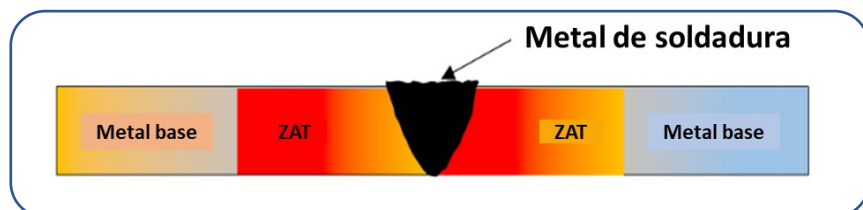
Perfil de la soldadura que muestra MB, HAZ y MS.
